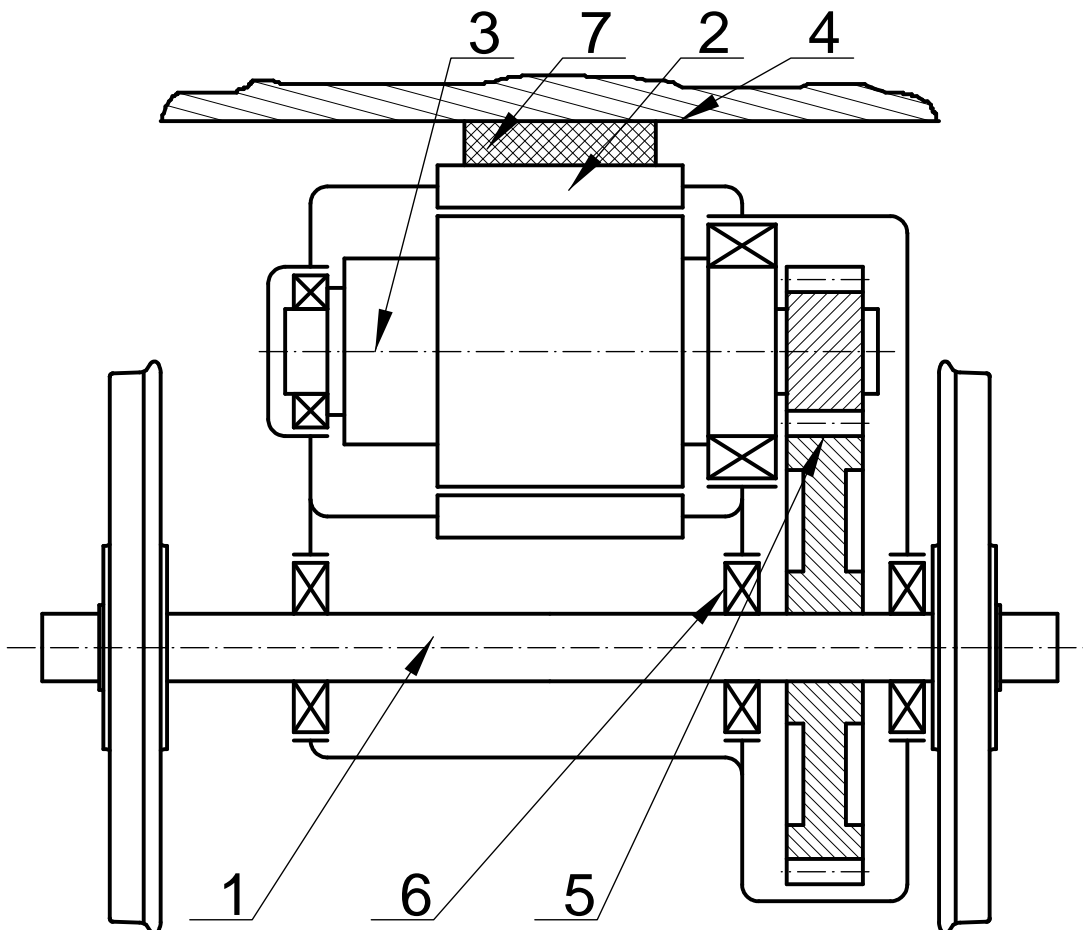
Schematický náčrt pohonu neodpruženým motorem; 1- dvojkolí, 2 - stator, 3 – rotor
